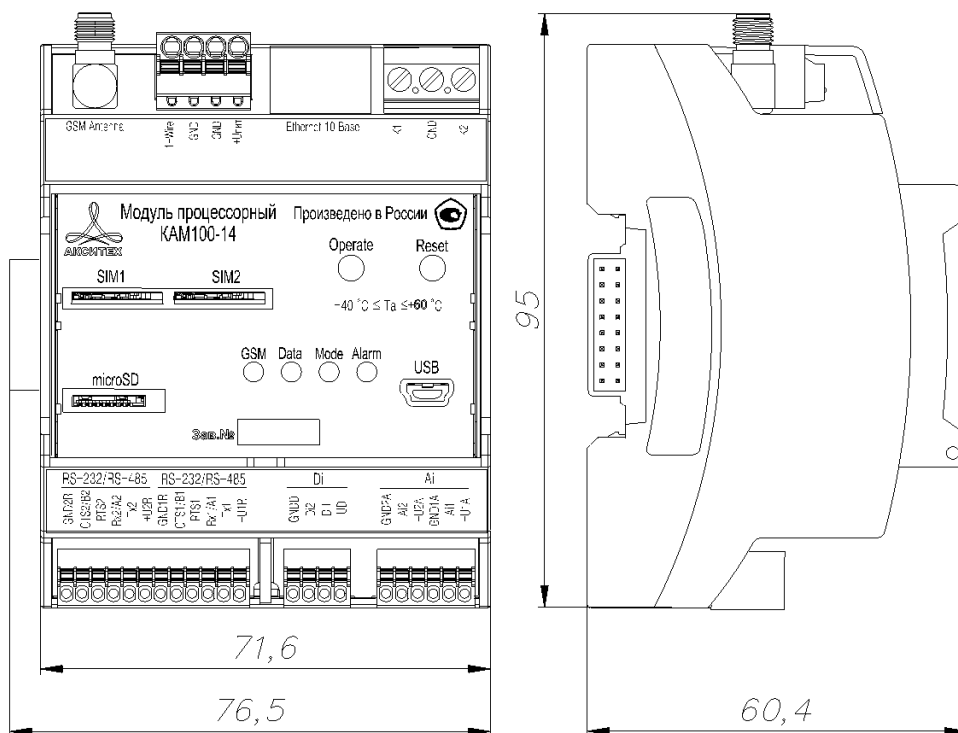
Внешний вид и габаритные размеры модуля процессорного КАМ100-14
